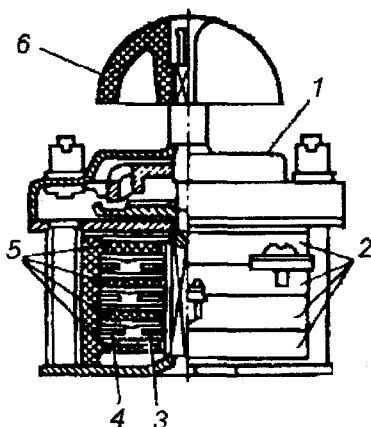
Пакетный выключатель: 1 – корпус; 2 – пакеты; 3 – подвижные контакты; 4 – неподвижные контакты; 5 – изоляционные перегородки; 6 – рукоятка
